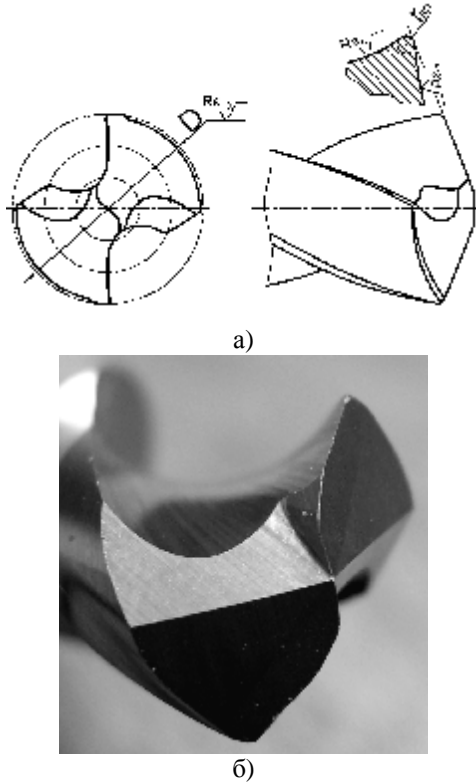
Робоча частини свердла: а) ескіз робочої частини; б) зовнішній вигляд
